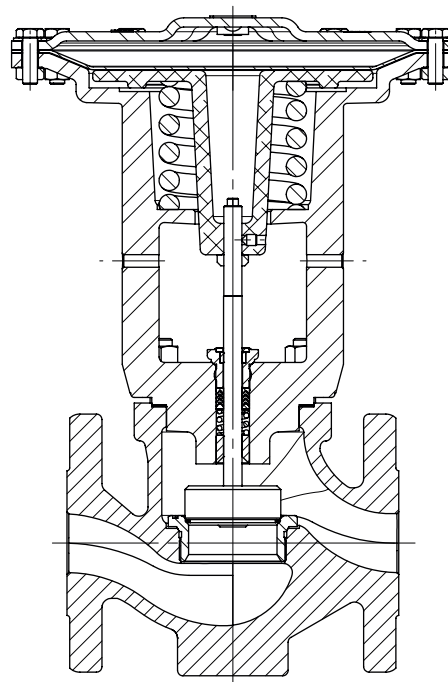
Vanne Tout ou Rien pneumatique type 3351 - Exécution „Ressort ouvre“
